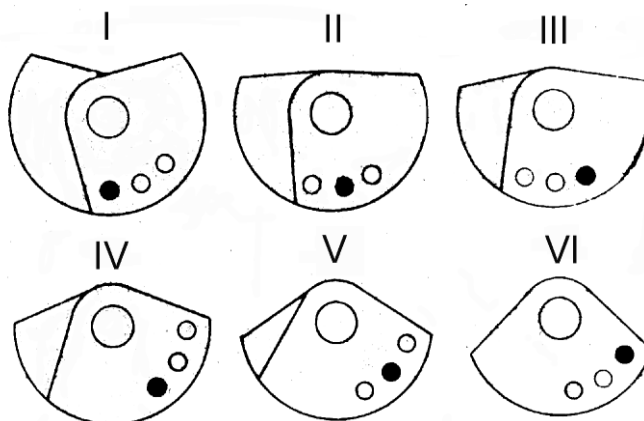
Схема регулировки статического момента для вибраторов ЭВВ-2,5-25; ЭВВ-06-25; ЭВВ-05-50; ЭВВ-11-50, ЭВВ-20-50.
